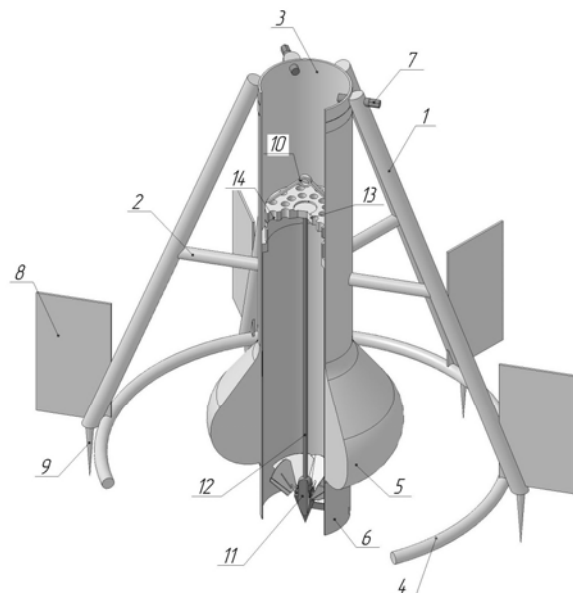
Загальний вид пробовідбірника: 1 – стрижень; 2 – розпірка; 3 – шахта колонкової труби; 4 – обвідне кільце; 5 – баласт; 6 – колонкова труба; 7 – обмежувач; 8 – стабілізуюче крило; 9 – анкер; 10 – петля; 11 – запірний механізм; 12 – штанга; 13 – кришка; 14 – дренажний отвір
